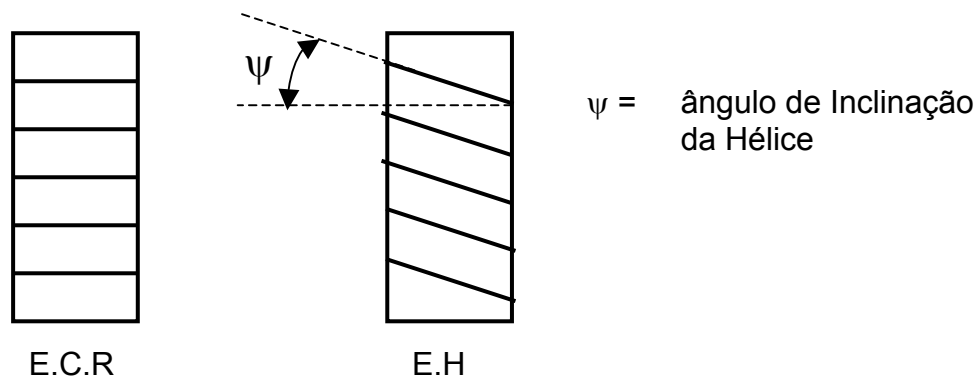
Engrenagens cilíndricas: reta e helicoidal
